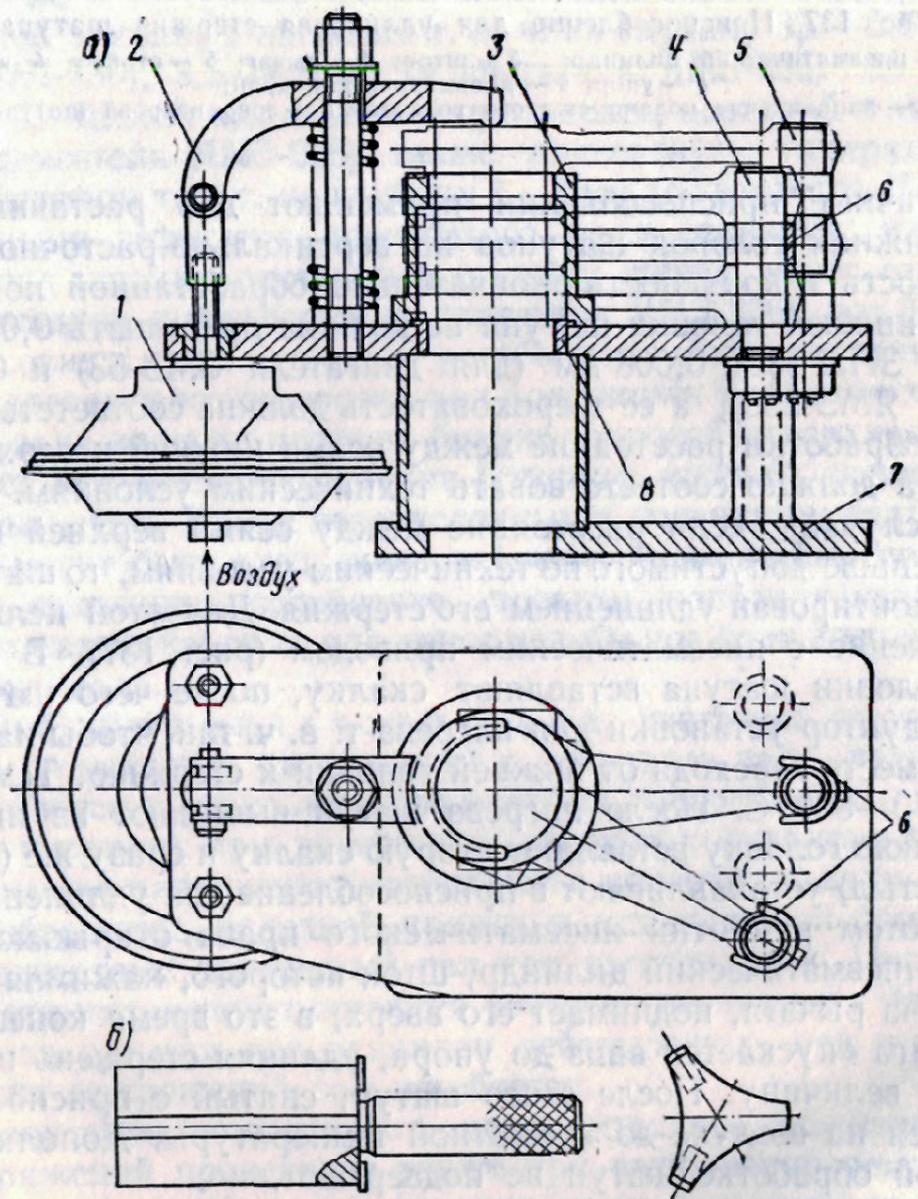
Приспособление для хонингования отверстий нижних головок шатунов двигателей:
